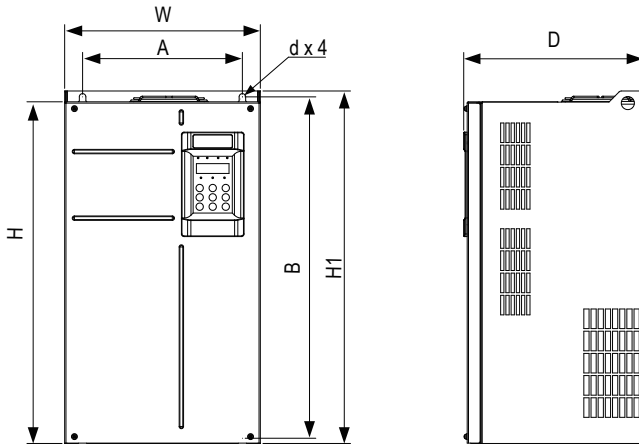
HVD100-4T45G/55P(B) ~ HVD100-4T160G/200P 外型尺寸及安装尺寸示意图
